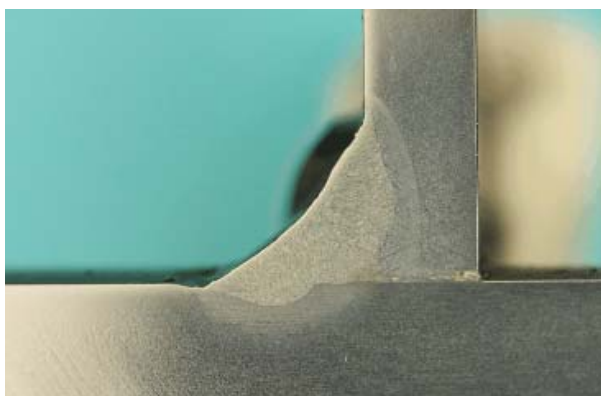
Macrografía de la soldadura mostrando falta de fusión en la raíz.
